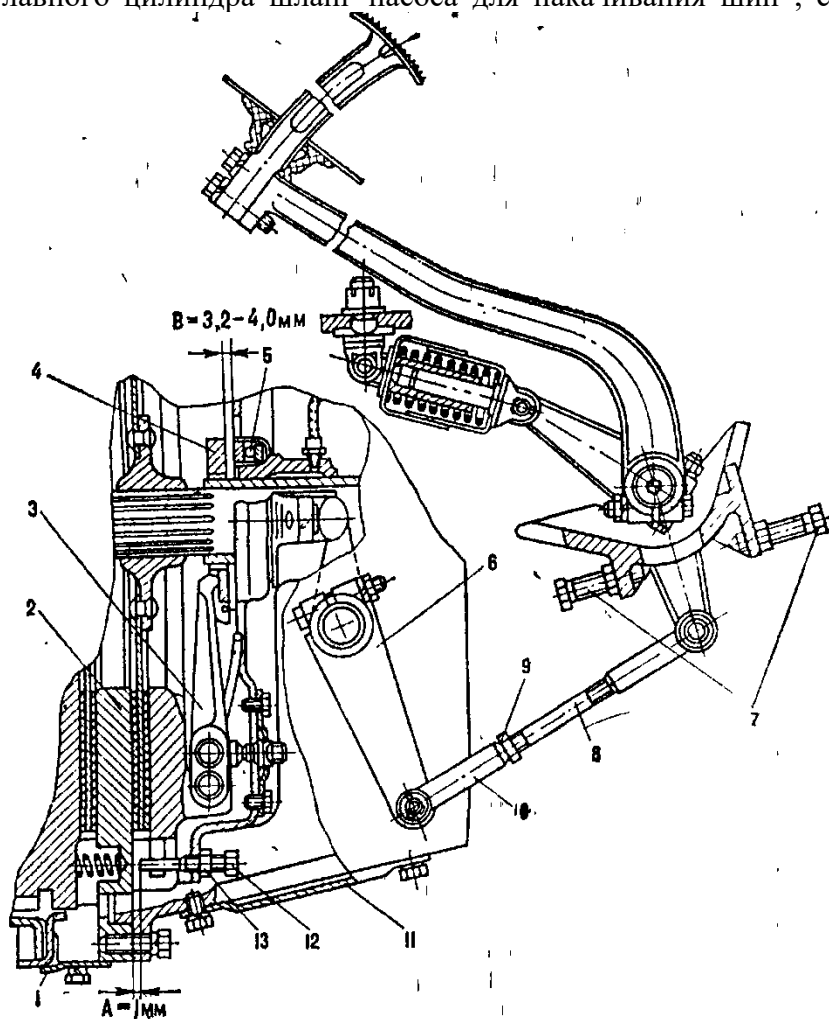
Регулировка сцепления автомобиля КрАЗ-257
